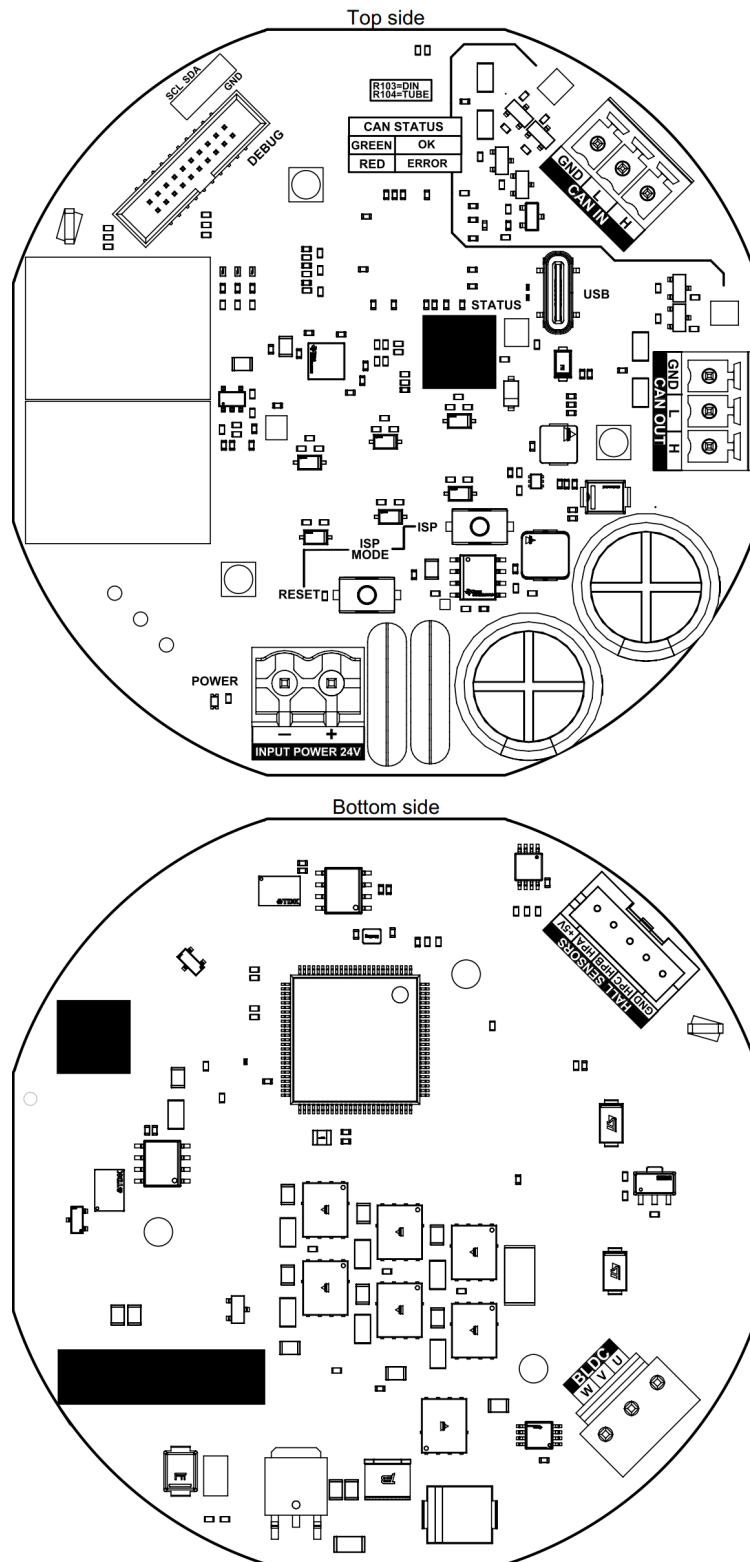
Anschlüsse des Erweiterungsmoduls BLDC TUBE
